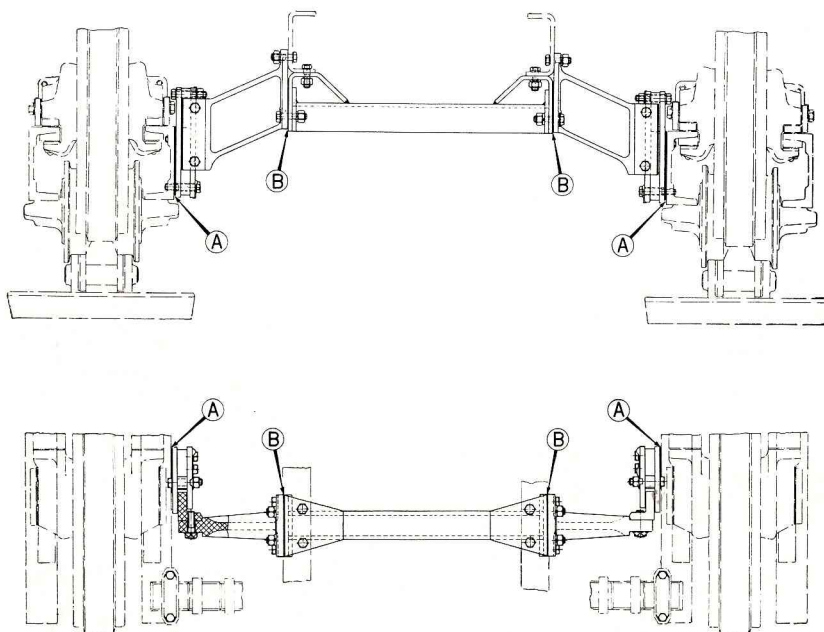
Barra di collegamento dei carrelli (Vista e pianta).
